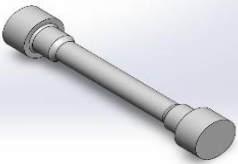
Dessin définition de l'éprouvette de la machine classique.
